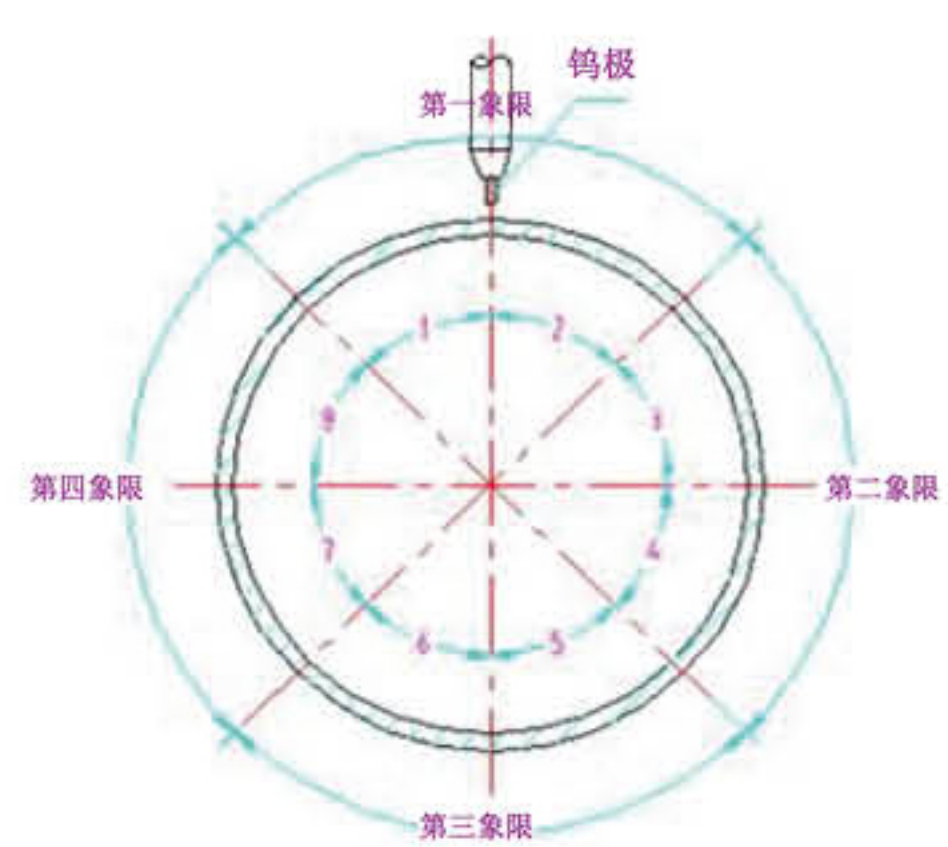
薄壁不锈钢管全位置焊接焊接区间划分图
